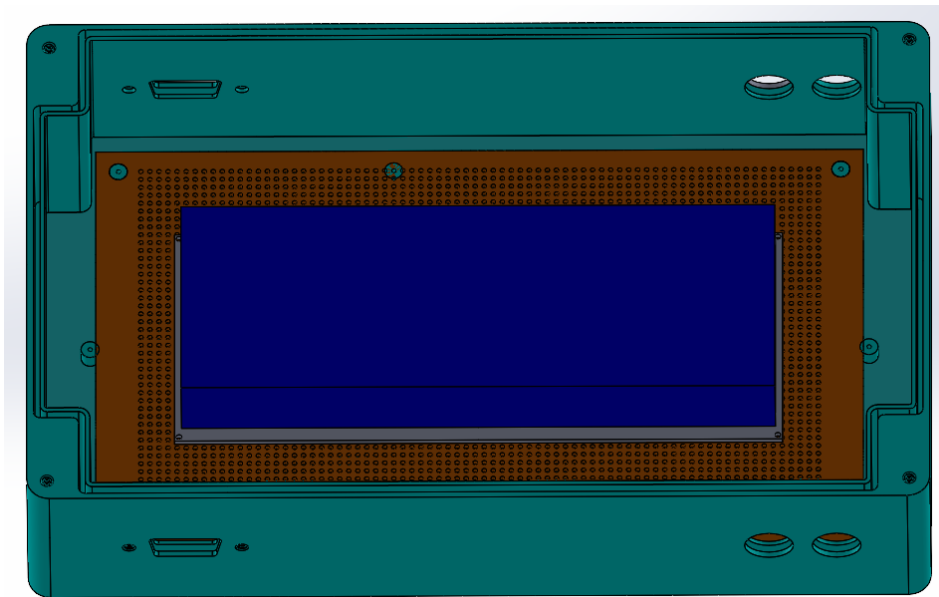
Fissaggio relay board a box con scheda millefori, progettato su Solidworks
